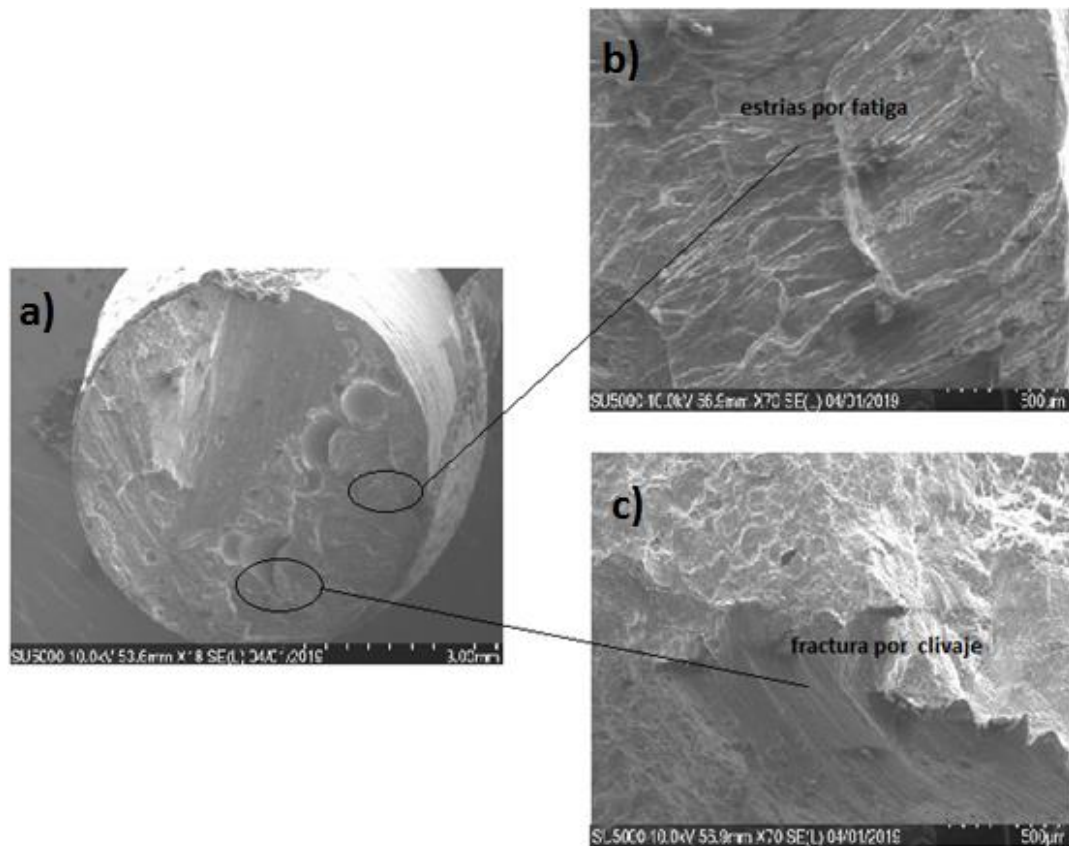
Imágenes del mecanismo de fractura por fatiga obtenidas de las juntas soldadas (a) fractura por fatiga (b) estrías de fatiga (c) fractura final.
